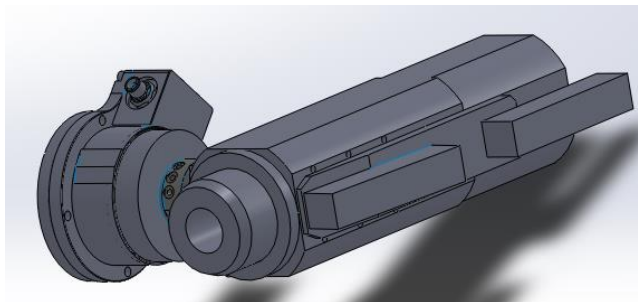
Assembly do conjunto terminal acoplado no robô.
